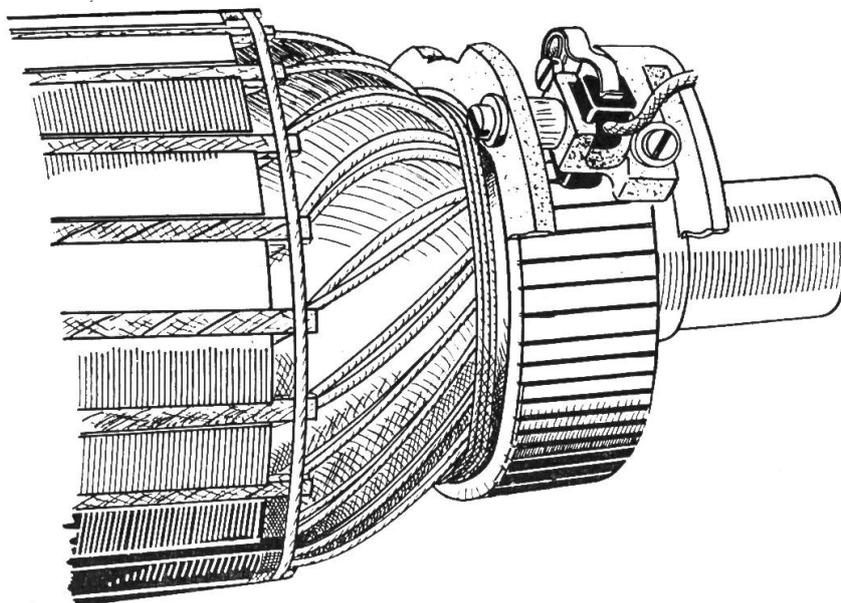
Detailansicht einer Schleifkohle. Die Kohle wird durch Federkraft leicht auf den Kollektor gedrückt. An ihrem Hinterende ist die Kupferleitung festgemacht.
